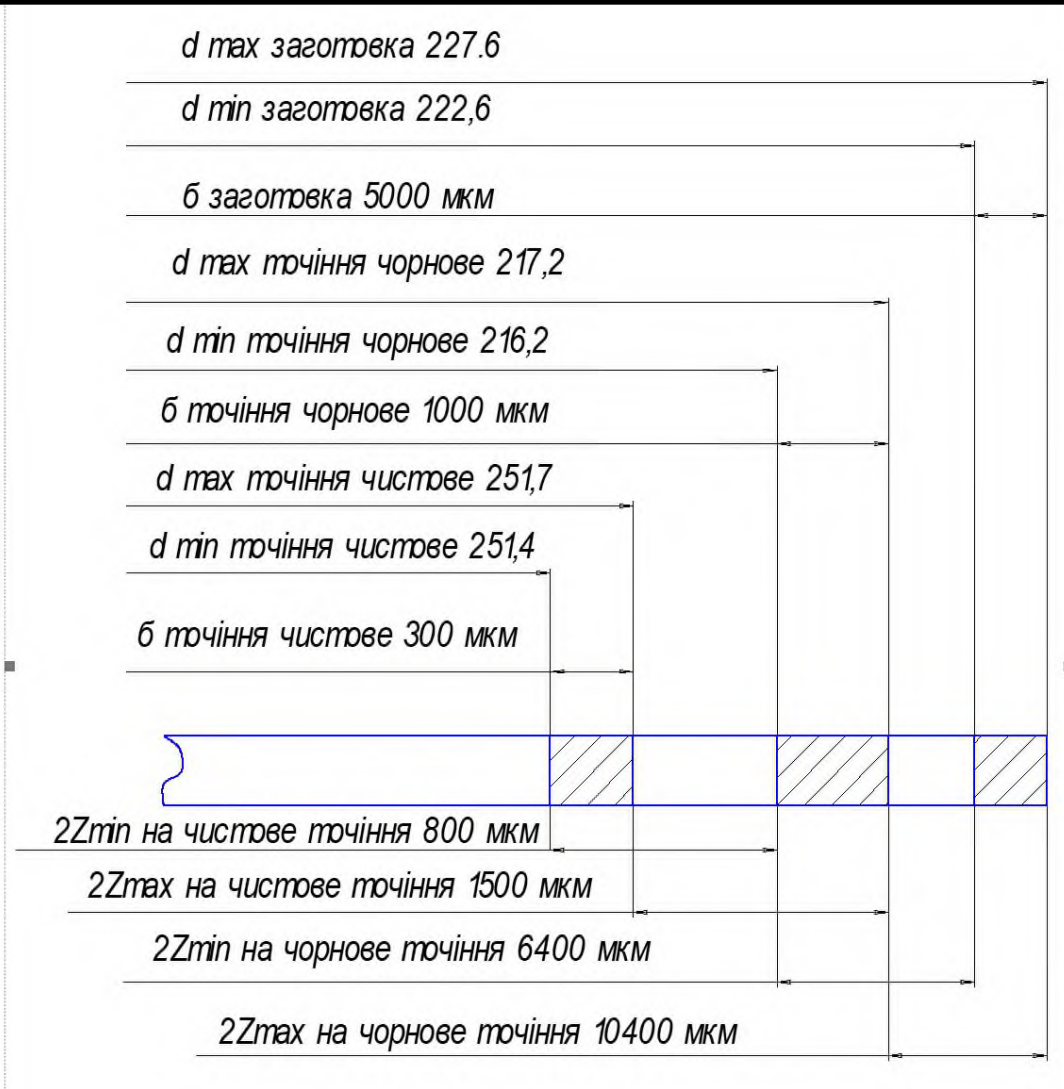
Схема розміщення припусків і полів допусків на обробку зовнішньої циліндричної поверхні.
